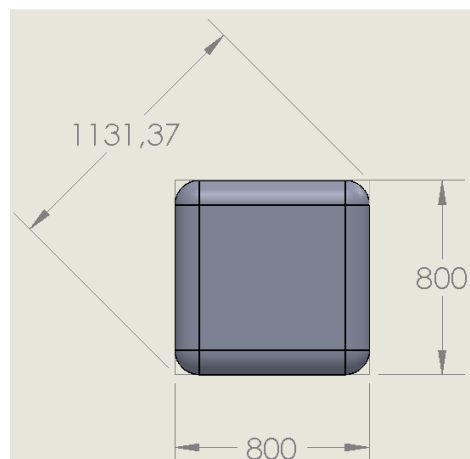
5.- Dimensiones del autoparte en posición horizontal
